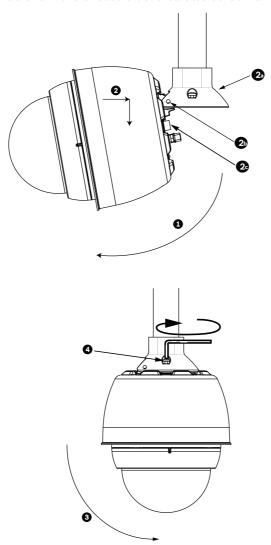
Fixation de la tête sur le support de montage parapet ou sur tube
